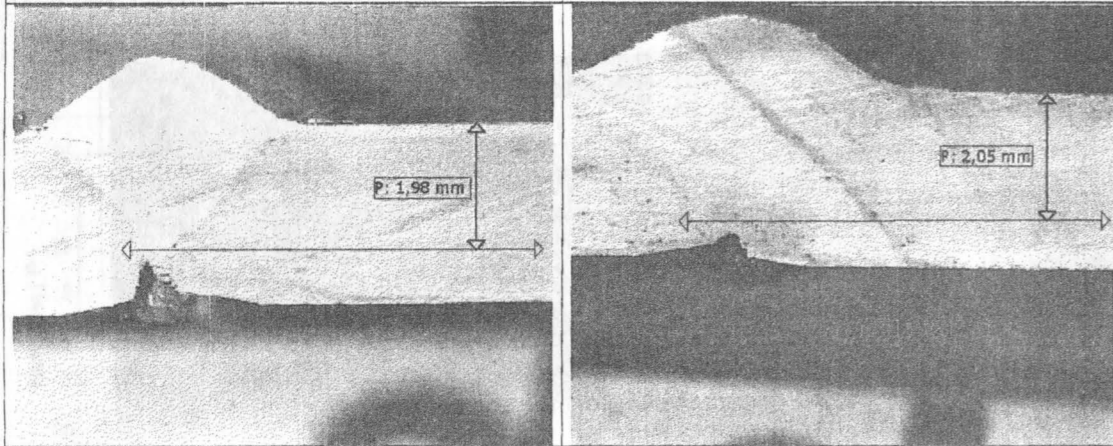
115 Amper kaynak akımı makroyapı fotoğrafı (X10)
